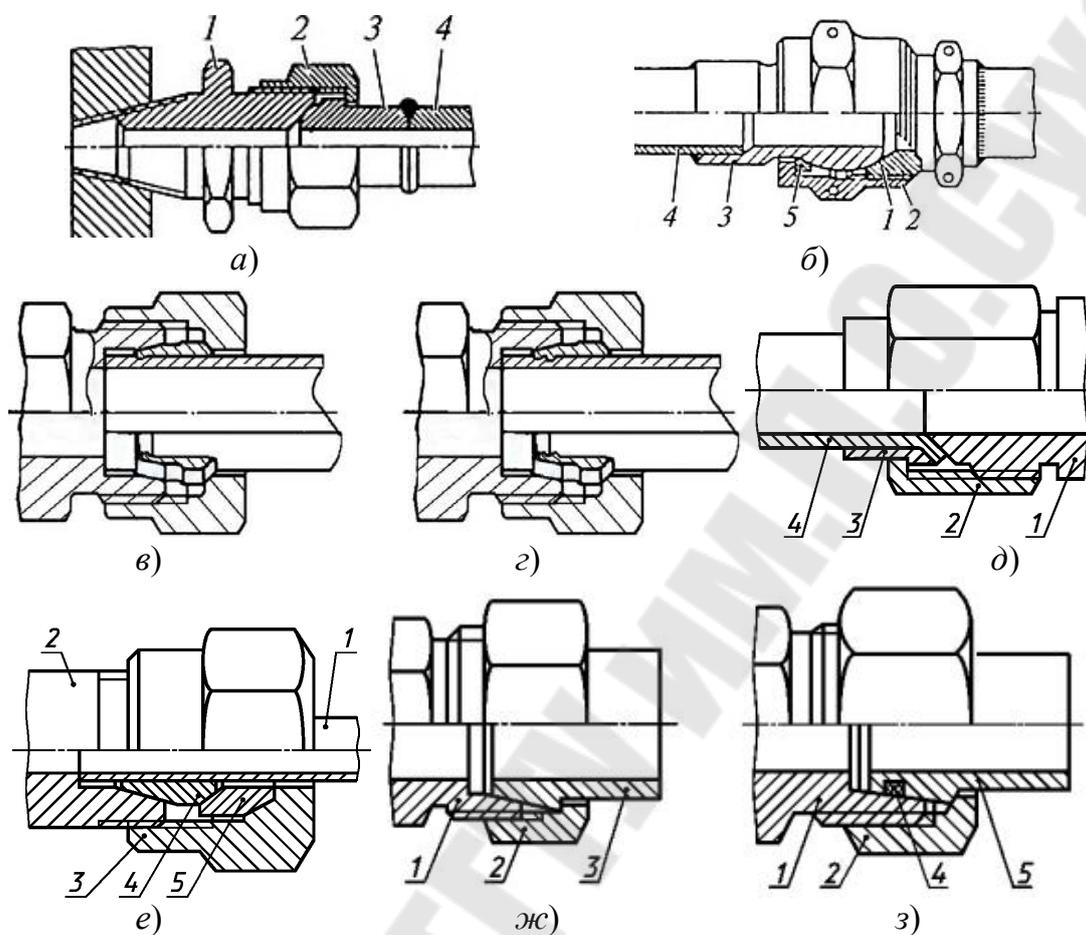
Виды резьбовых соединений: а) сфера по конусу с шаровым ниппелем с полусферой; б) сфера по конусу с шаровым ниппелем с полной сферой; в) с одним врезным кольцом; г) с двумя врезным кольцом; д) с уплотняющей отбортовкой; е) с зажимным кольцом; ж, з) с коническим штуцером под сварку;
